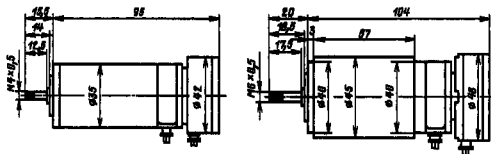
Габаритные и установочные размеры двигателей ДПР-62 с ТИ(ТС) и ДПР-7 с ТИ
